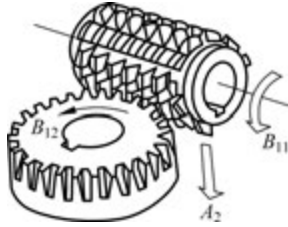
用齿轮滚刀加工直齿圆柱齿轮
